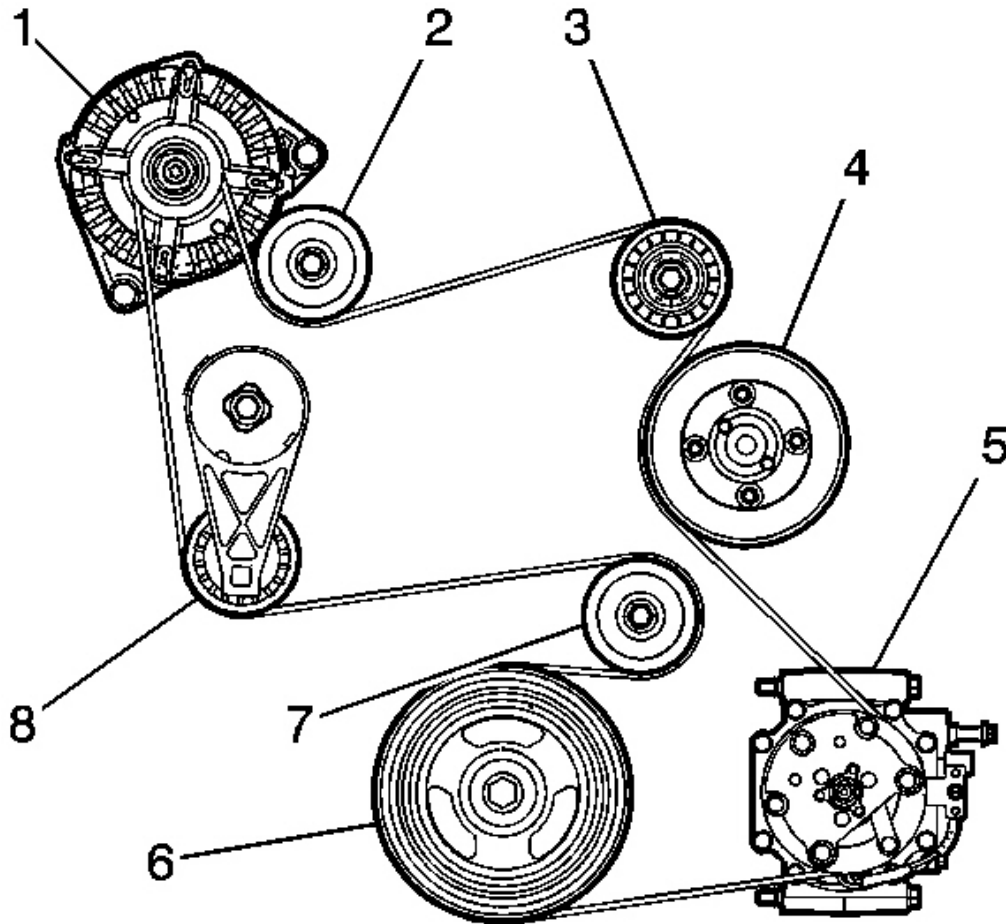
Vista de la correa de la polea loca izquierda
